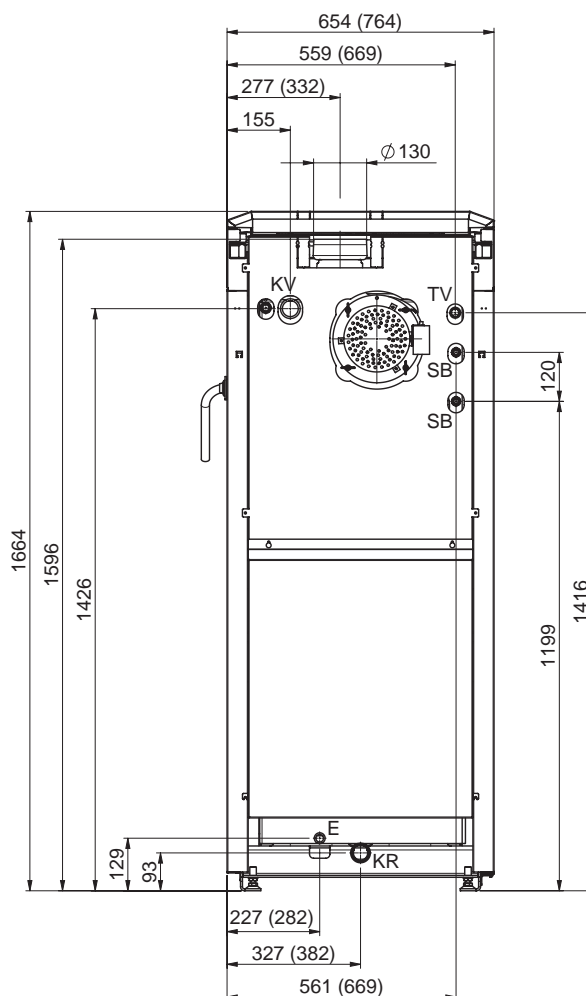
Ventilateur de fumées monté directement sur la chaudière LogWIN Premium Touch – vue de la face arrière
